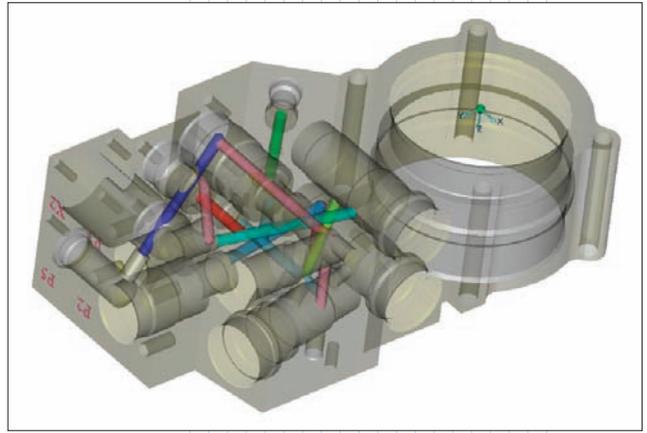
Модель для многопозиционной фрезерной и сверлильно-расточной обработки
